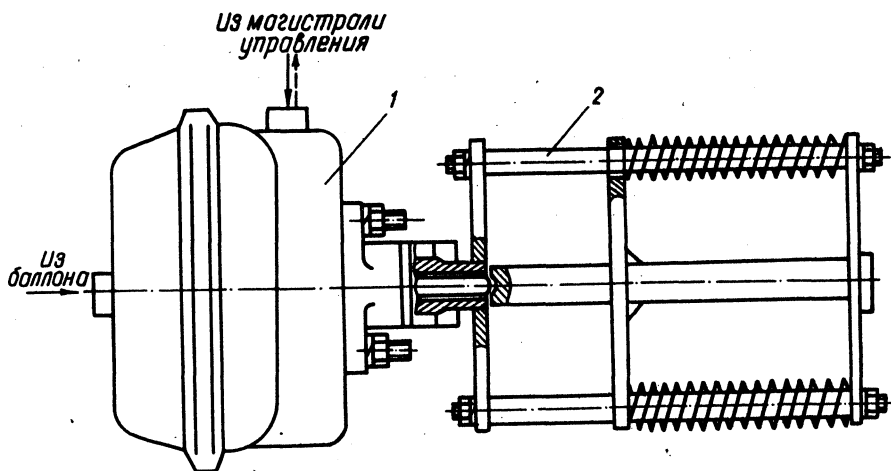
Приспособление для износных испытаний пневматического переходника:
